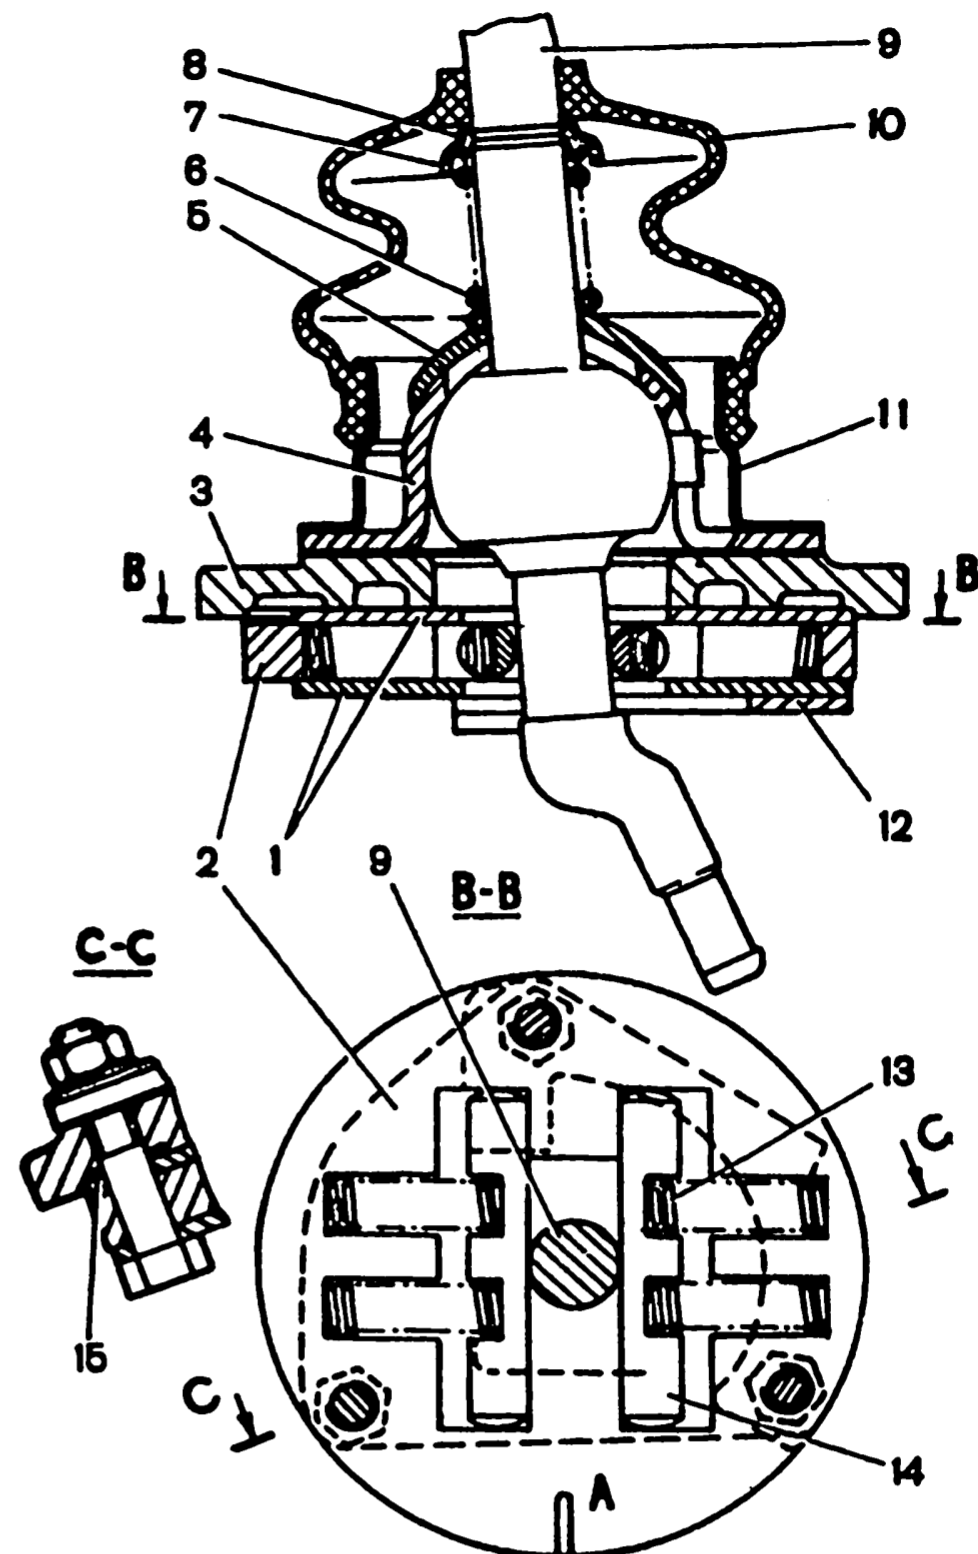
Механизм выбора передач: 1 - шайбы направляющей пластины; 2 - направляющая пластина рычага переключения передач; 3 - корпус рычага переключения передач; 4 - шаровая опора рычага; 5 - сферическая шайба; 6 - пружина; 7 - стопорное кольцо; 8 - стопорное кольцо; 9 - рычаг переключения передач; 10 - защитный чехол; 11 - фланец; 12 - блокировочная пластина заднего хода; 13 - пружина; 14 - направляющая планка; 15 - уплотнительное кольцо; А - риска
